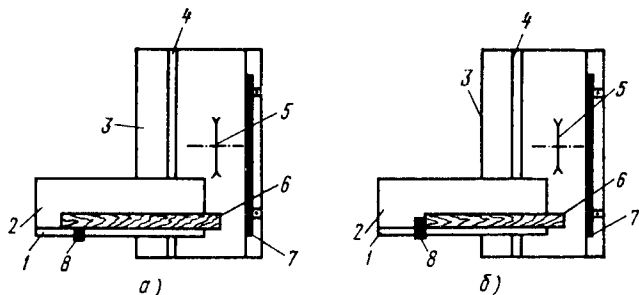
Торцовка заготовок на однопильном торцовочном станке с кареткой:
